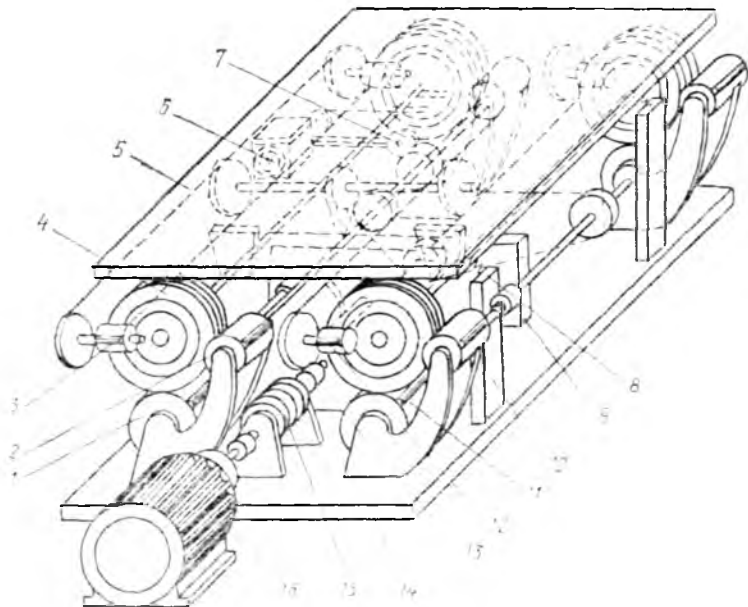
Схема стенда для испытания кабин (МТЗ)
